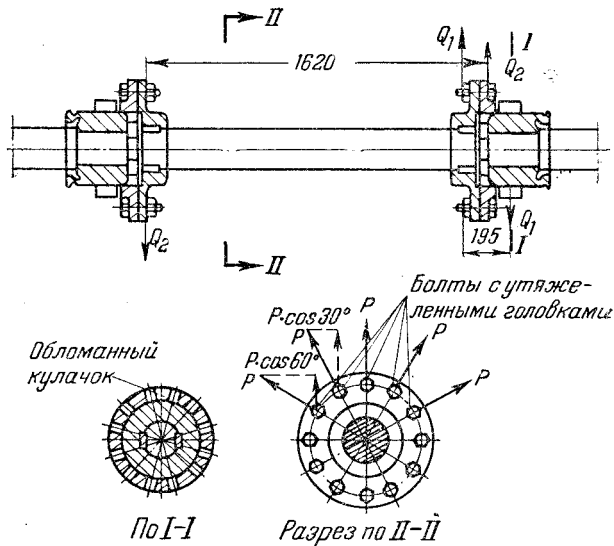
Соединительный вал турбовоздуходувки с кулачковыми муфтами.
